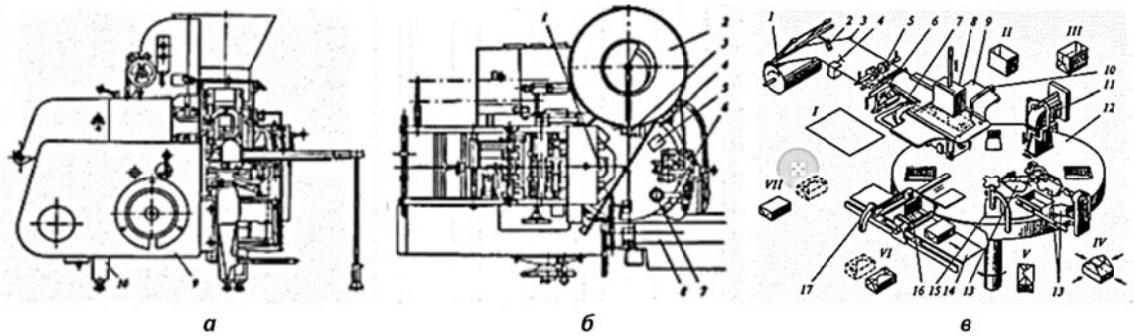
Машина АРТ для фасування сиру: *а* – вид фронтальний; *б* – вид зверху: 1 – механізм формування тари (пачки); 2 – бункер; 3 – дозатор; 4 – ротор; 5 – гнізда; 6 – механізм укладання пачки; 7 – механізм підпресування; 8 – транспортер; 9 – станина; 10 – опора; *в* - технологічна схема: 1 – рулон пергаменту; 2 – механізм притиску; 3 – валик напрямний; 4 – маркер; 5 – валики регульовальні; 6 – ножі; 7 – важелі; 8 – пуансон; 9 – матриця формування пачки; 10 – щуп; 11 – дозатор об'ємний; 12 – ротор; 13 – механізм загортання пачки; 14 – транспортер; 15 – механізм підпресування; 16 – механізм повороту; 17 – знімач
